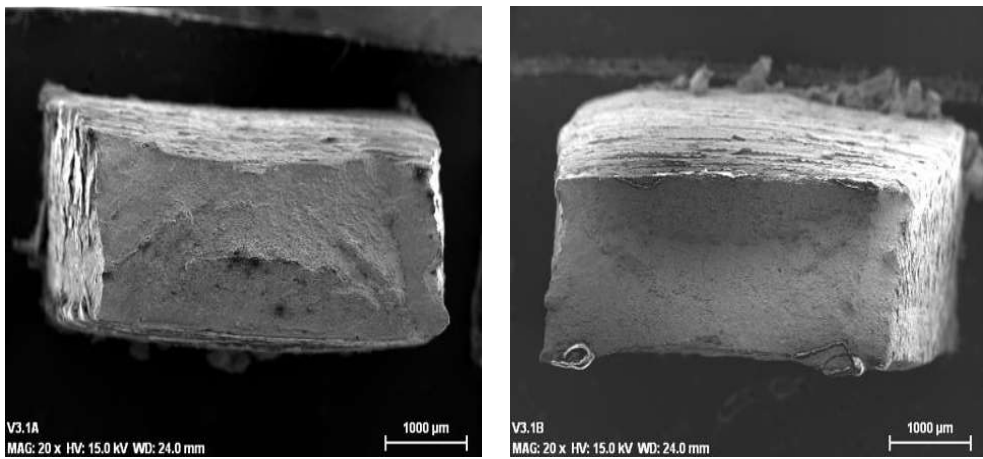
Fractografía de la unión a 75°, probeta 1.
